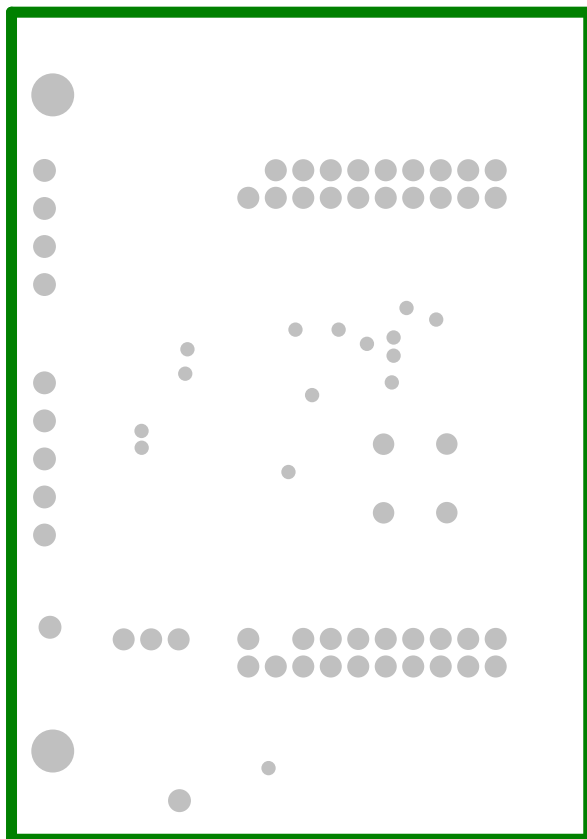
ADS122x14EVM 的 PCB 布局 (内部 GND 平面 1)
